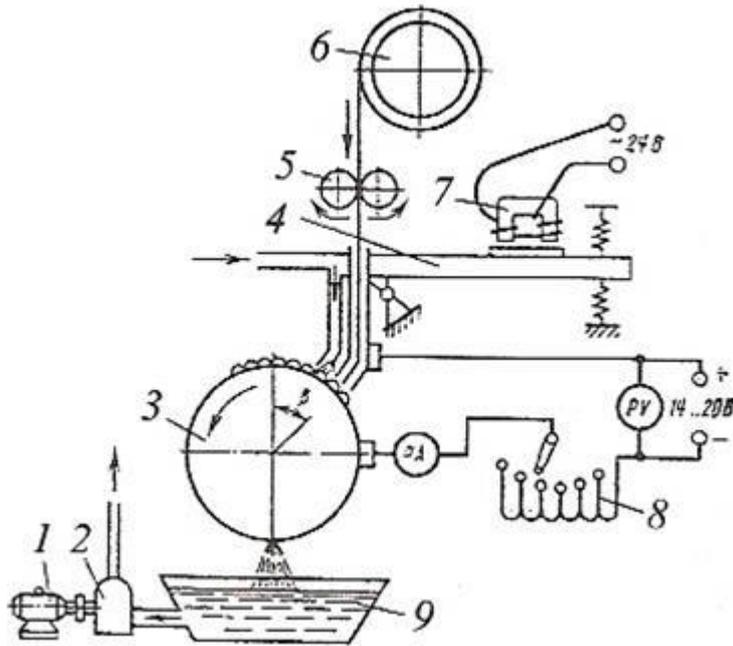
Схема вибродуговой наплавки: 1— электродвигатель; 2— насос; 3 - наплавляемая деталь; 4 —вибрирующий мундштук; 5 - механизм подачи проволоки; 6— кассета; 7— вибратор; 8— индуктивное сопротивление; 9 -ванна для охлаждающей жидкости
